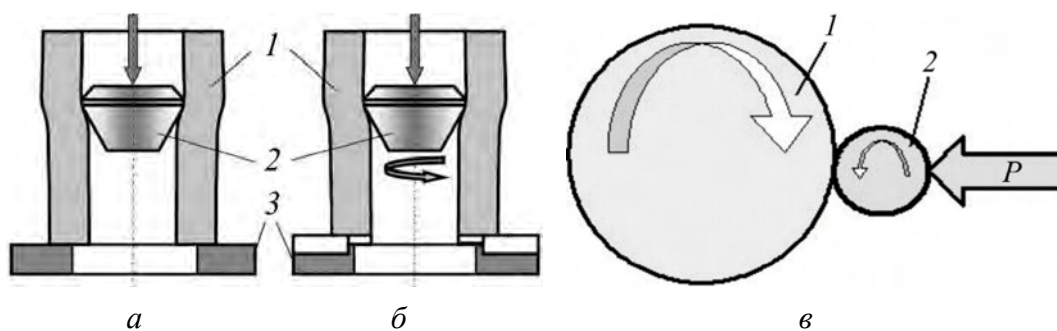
Схема деформирующего протягивания (а), протягивания с вращением (б) и накатки (в): 1 – образец, 2 – инструмент, 3 – опора
